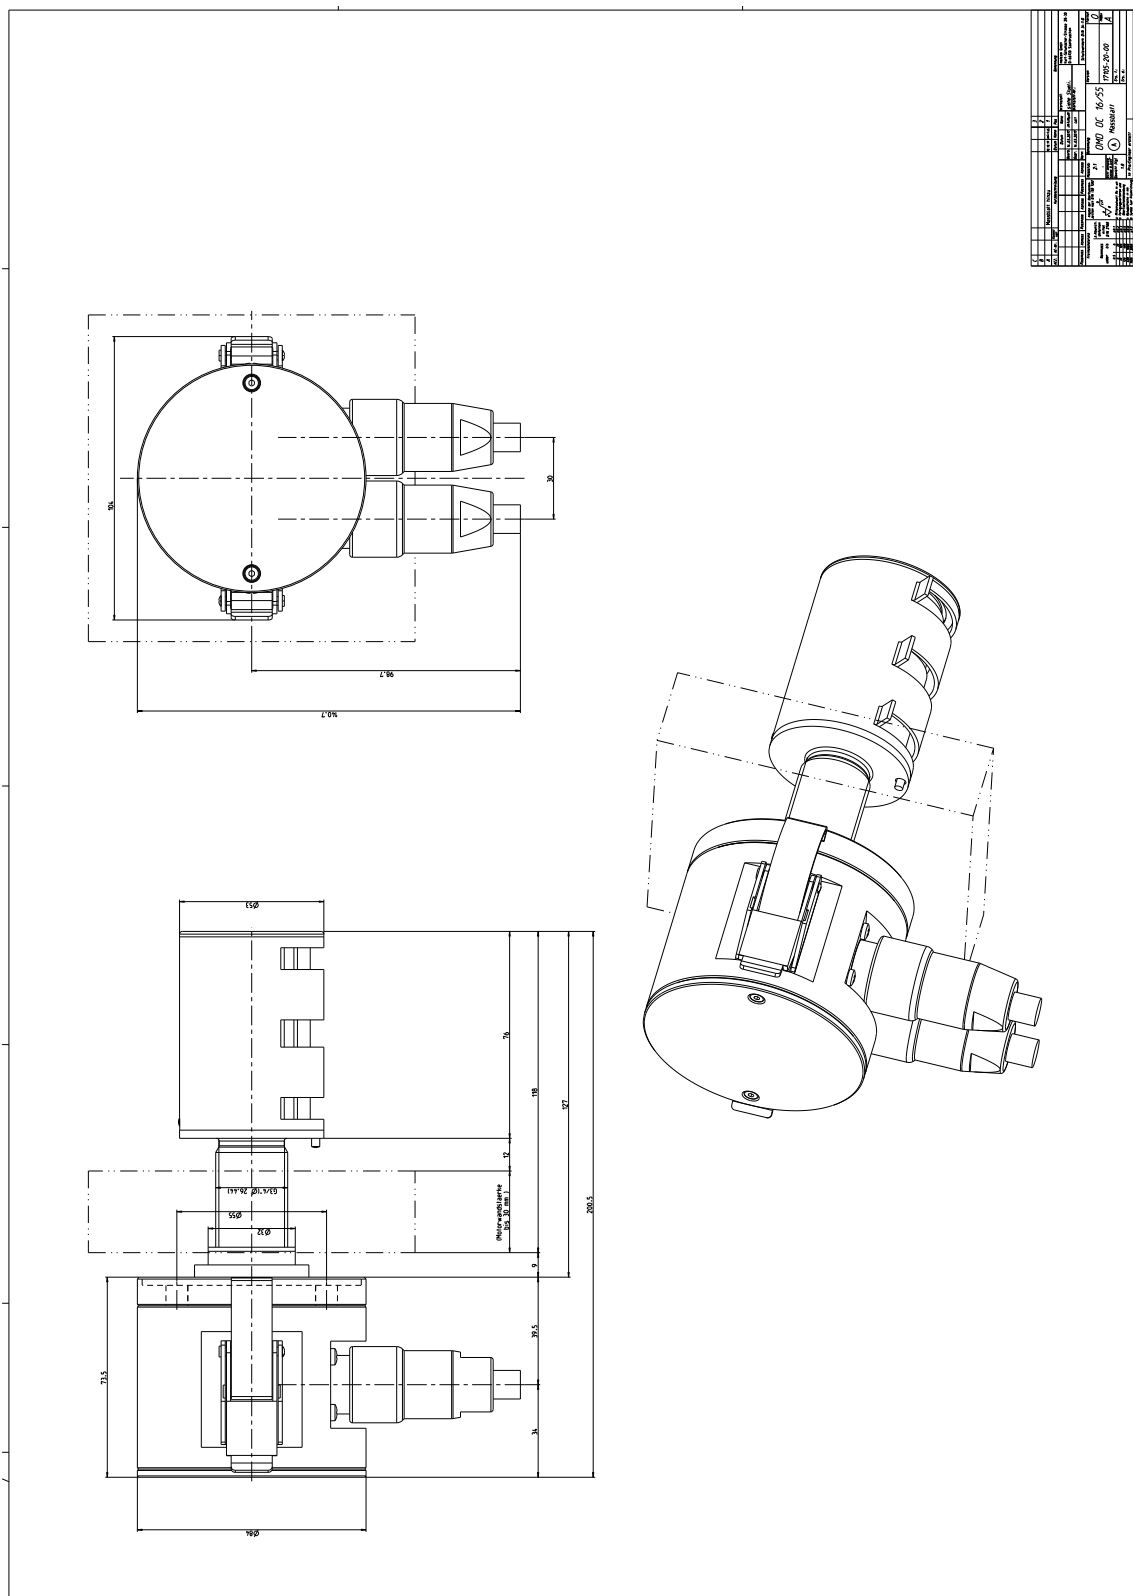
Dimensiones del sensor SiCOMS® de tipo SiSe/OC16-55
